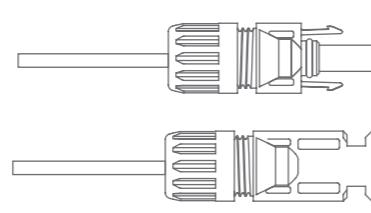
Stecker mit aufgeschraubter Überwurfmutter
